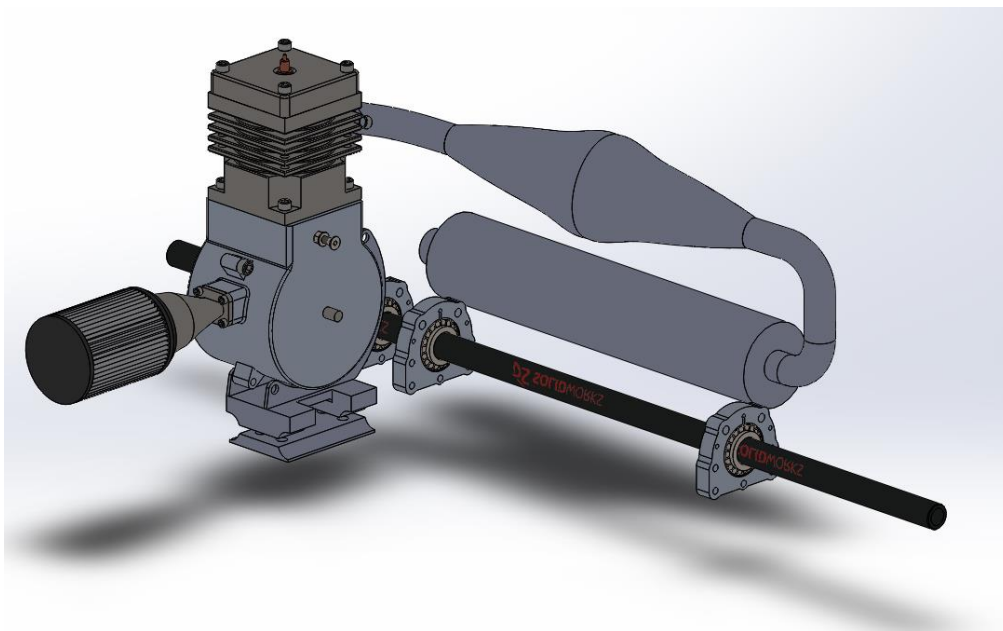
conjunto sistema de transmisión. Fuente: propia.
